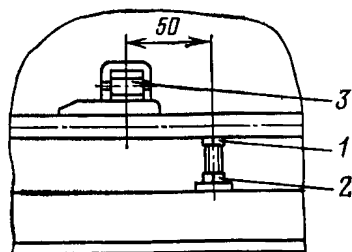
Схема установки упорного болта: 1 — болт М10×45; 2 — гайка М10; 3 — упор блокирующего устройства
